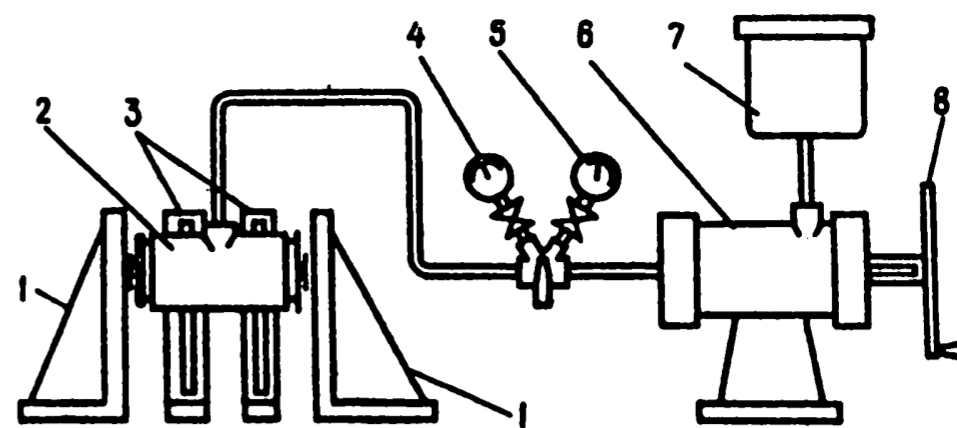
Схема проверки колесных цилиндров задних тормозов: 1 - упоры поршней; 2 - испытуемый цилиндр; 3 - кронштейн цилиндра; 4 - манометр низкого давления; 5 - манометр высокого давления; 6 - цилиндр для создания давления; 7 - сосуд; 8 - маховик
